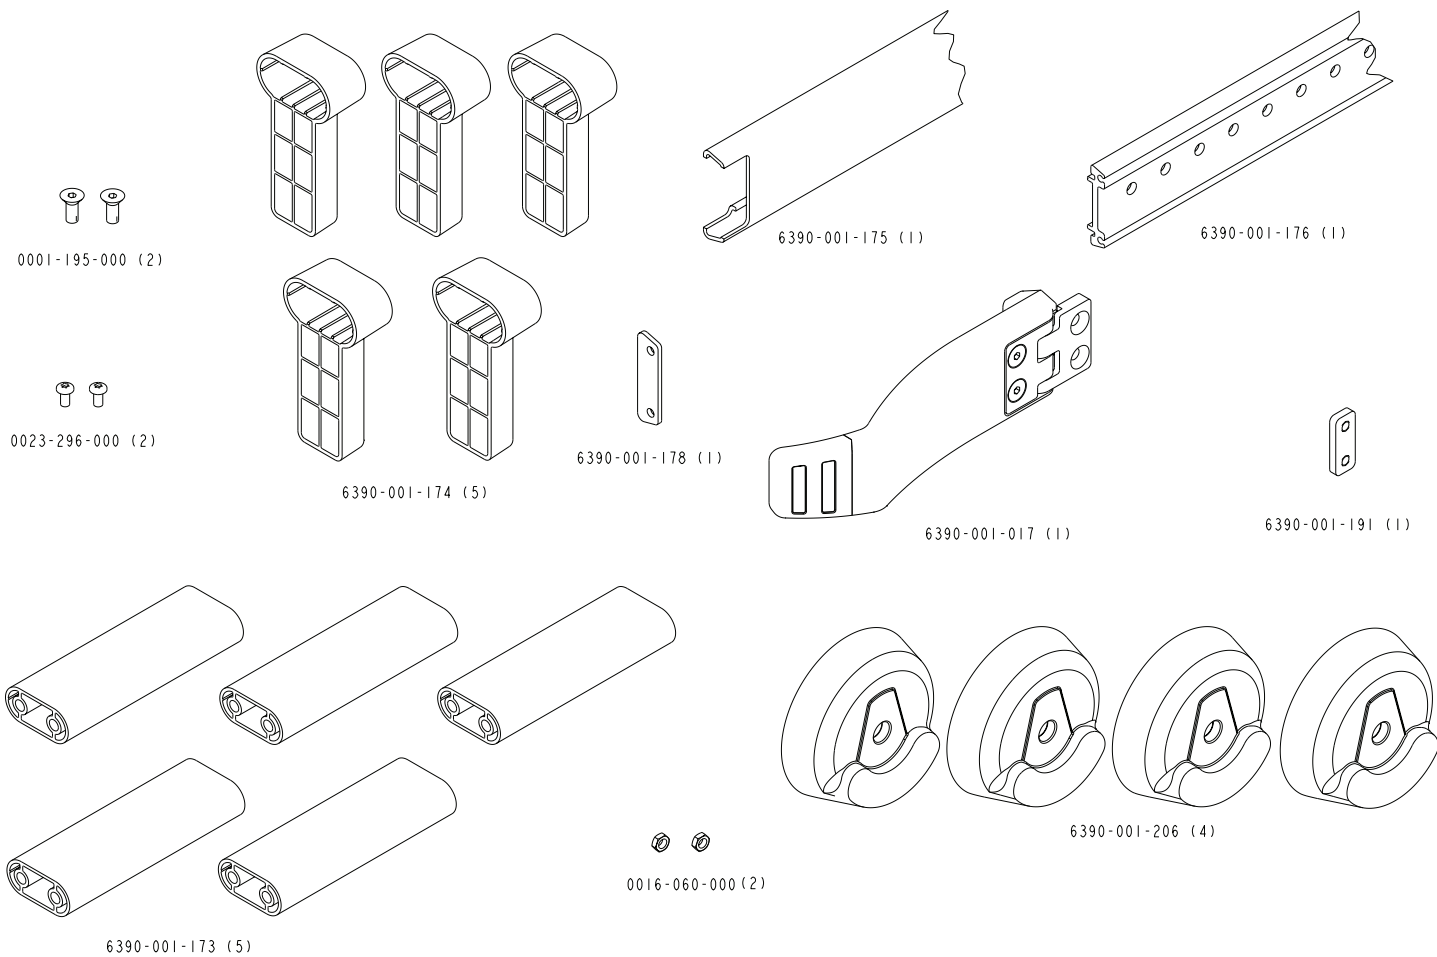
Componentes do kit de instalação do conjunto de guia das rodas opcional 6390-027-000
